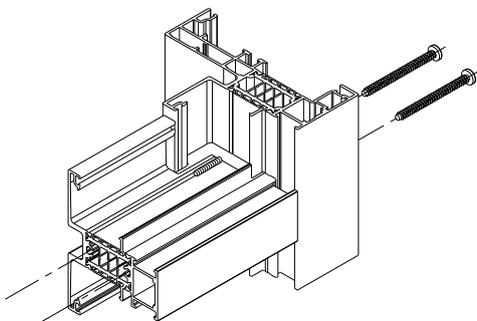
## DETAILS ETANCHEITE DANS ASSEMBLAGE TRAVERSES / MENEAUX
